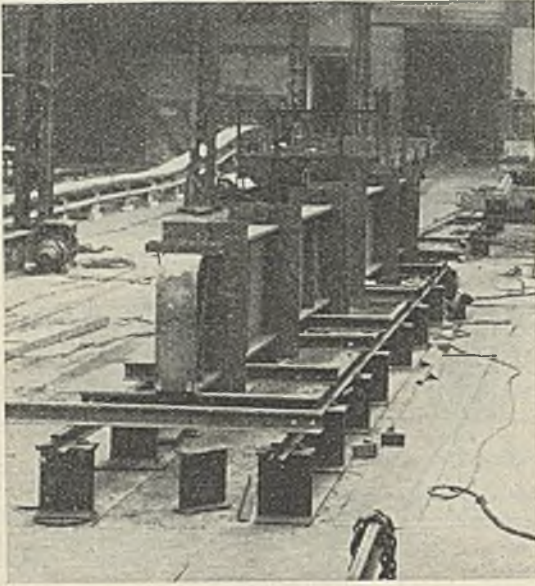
Hauptträger, mit eisernen Schablonen zusammengehalten.
